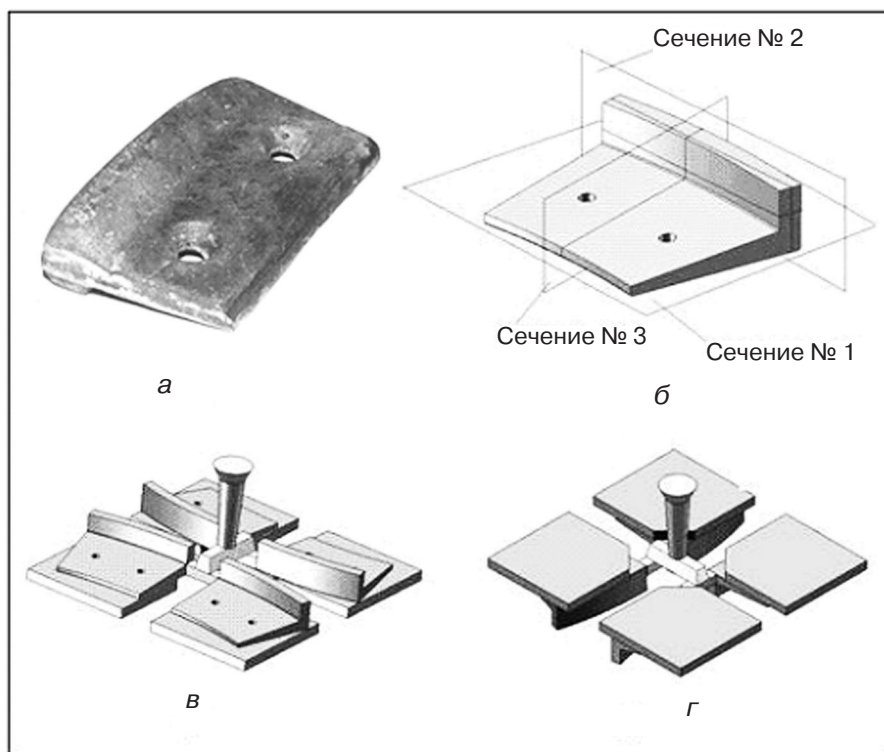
Отливка «Накладка» (а); 3D модель и схема ее сечений (б); положение отливки в формах № 1 (в) и 2 (г)
